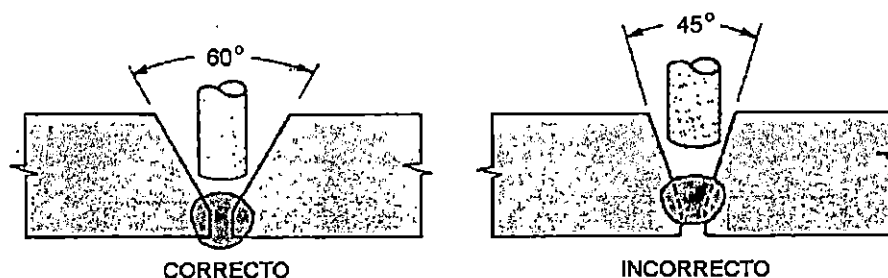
Para obtener una buena soldadura debe utilizarse la abertura adecuada.
